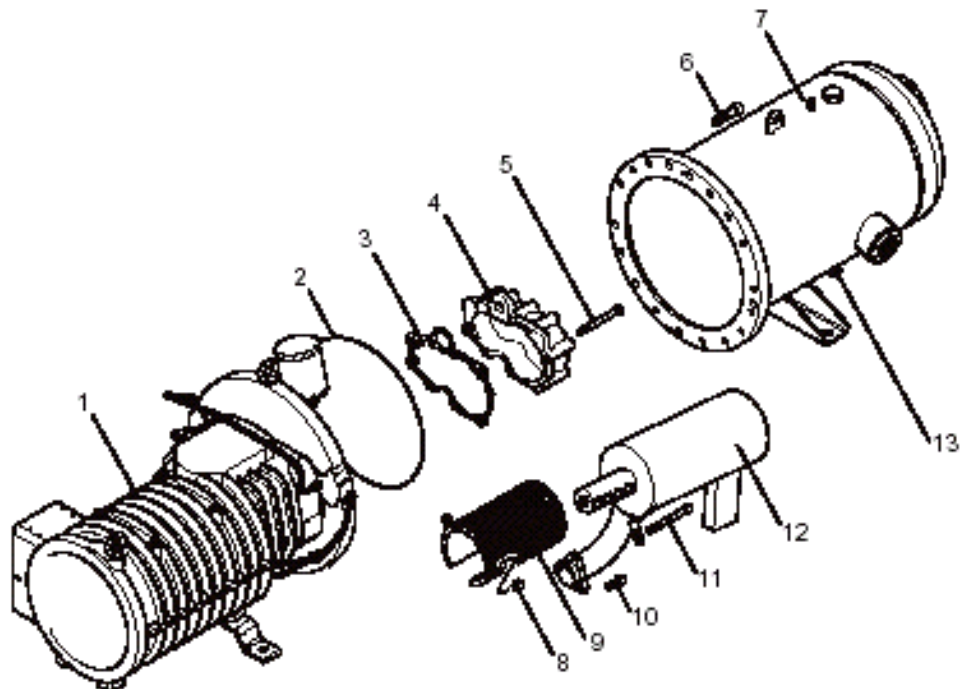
Desmontagem e montagem de um compressor parafuso; exemplo: compressor parafuso compacto HSKC 74
